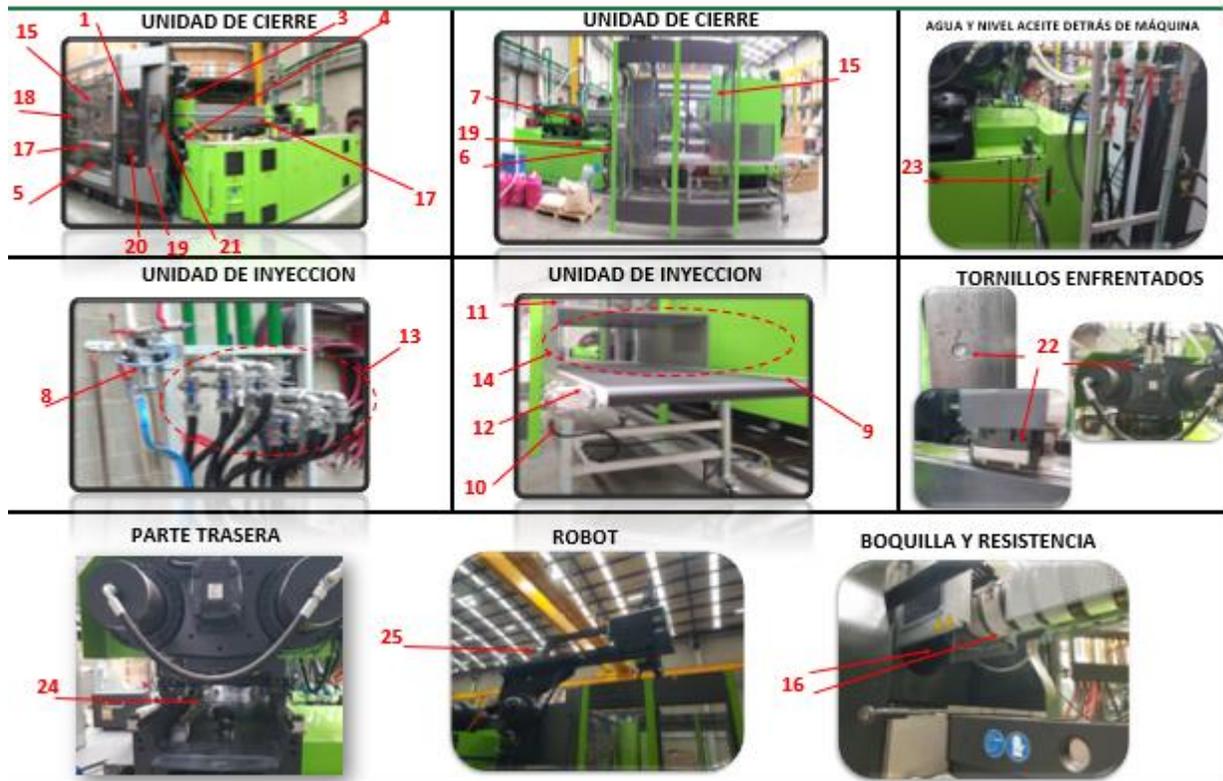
Ayuda visual de partes a inspeccionar en la ruta de inspección.
